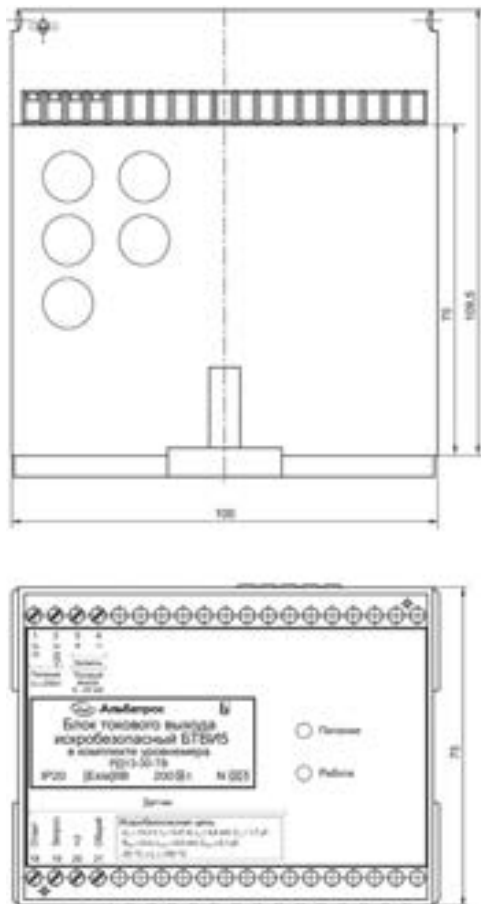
Габаритные размеры блока БТВИ5
